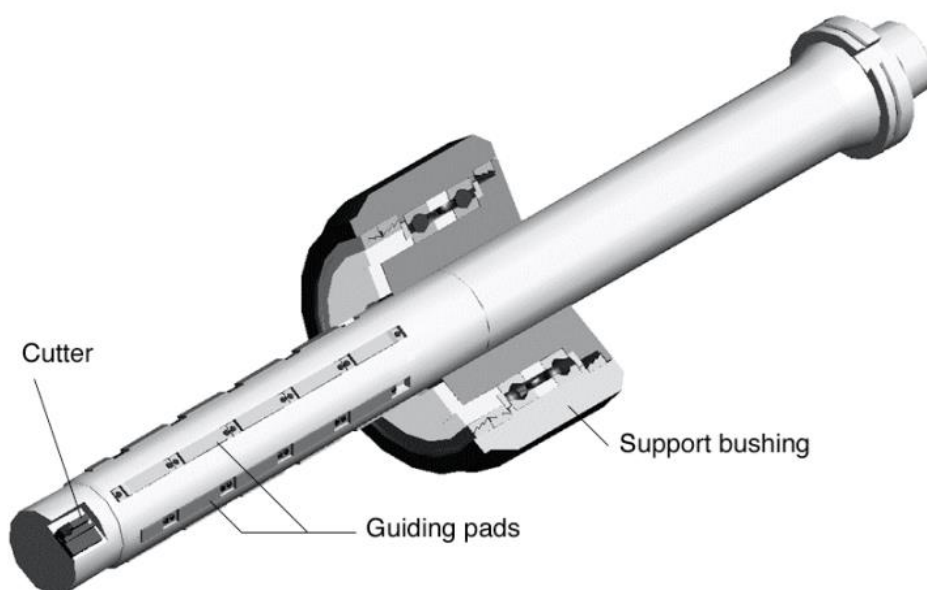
Розточний інструменти із напрямними опорами [28]
